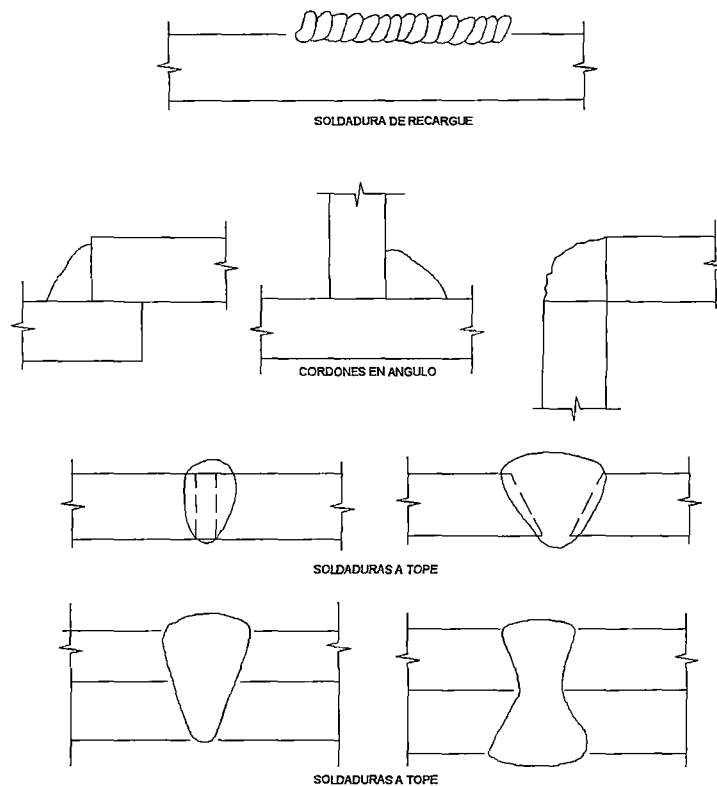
TIPOS DE SOLDADURAS
